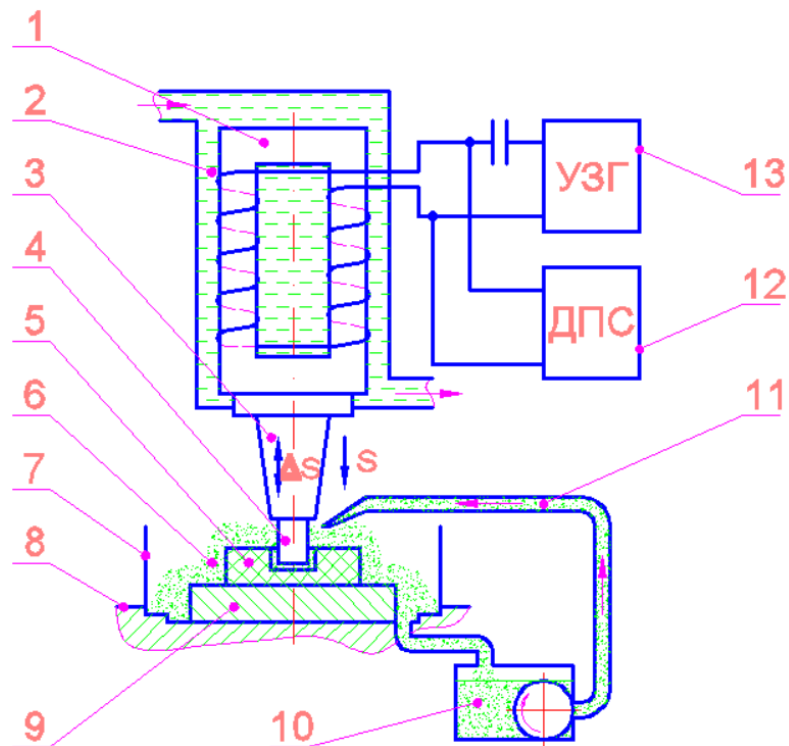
Схема ультразвукового прошивального верстата: 1 – перетворювач ультразвукових коливань; 2 – головка верстата з охолоджуваною рідиною; 3 – концентратор енергії ультразвукових коливань; 4 – інструмент; 5 – заготовка; 6 – абразивна суспензія; 7 – захисний кожух; 8 – стіл верстата; 9 – підкладка; 10 – бак з мішалкою та помпою; 11 – патрубок; 12 – джерело постійного струму; 13 – ультразвуковий генератор
